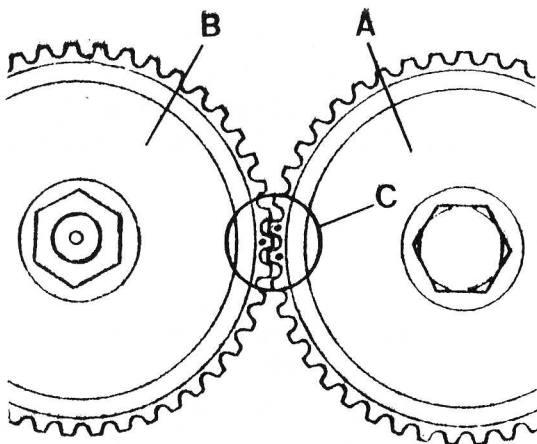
Posición de los engranajes de la distribución para -- proceder a su desmontaje
